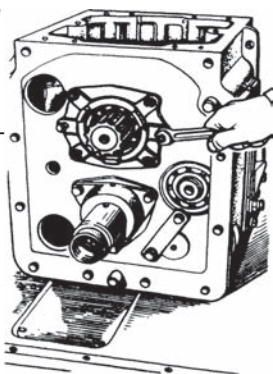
Снятие стопорного кольца подшипника первичного вала.
